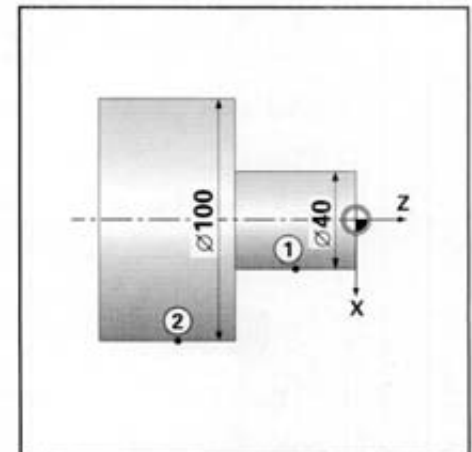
Werkstück-Zeichnung zum Beispiel "Aufmaße"; Werkzeug-Positionen ohne Auf- oder Untermaß
